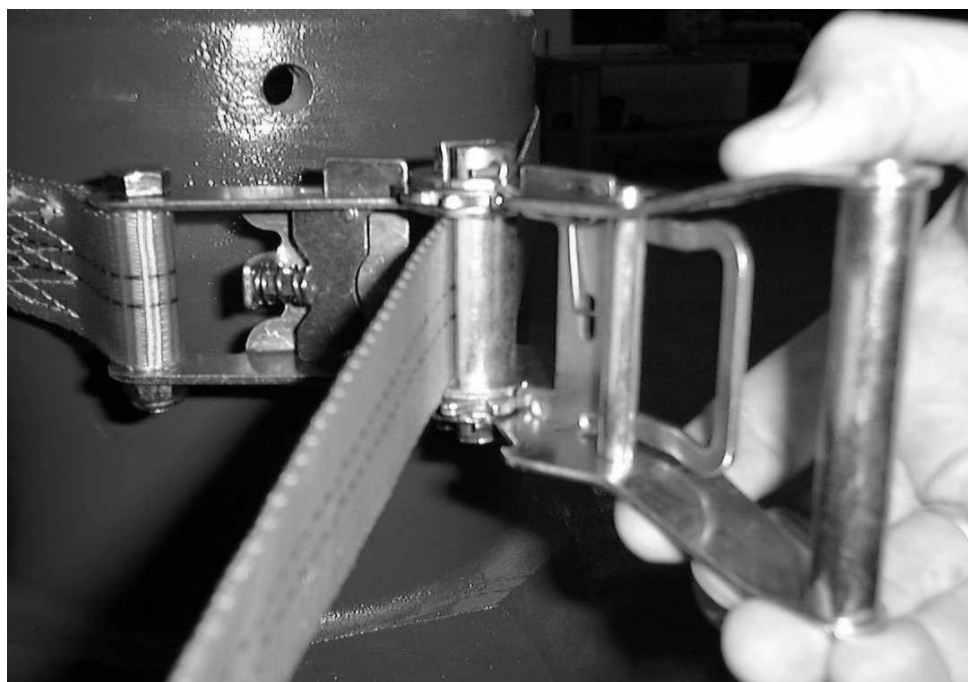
Установка приспособления "стойка воротника"
